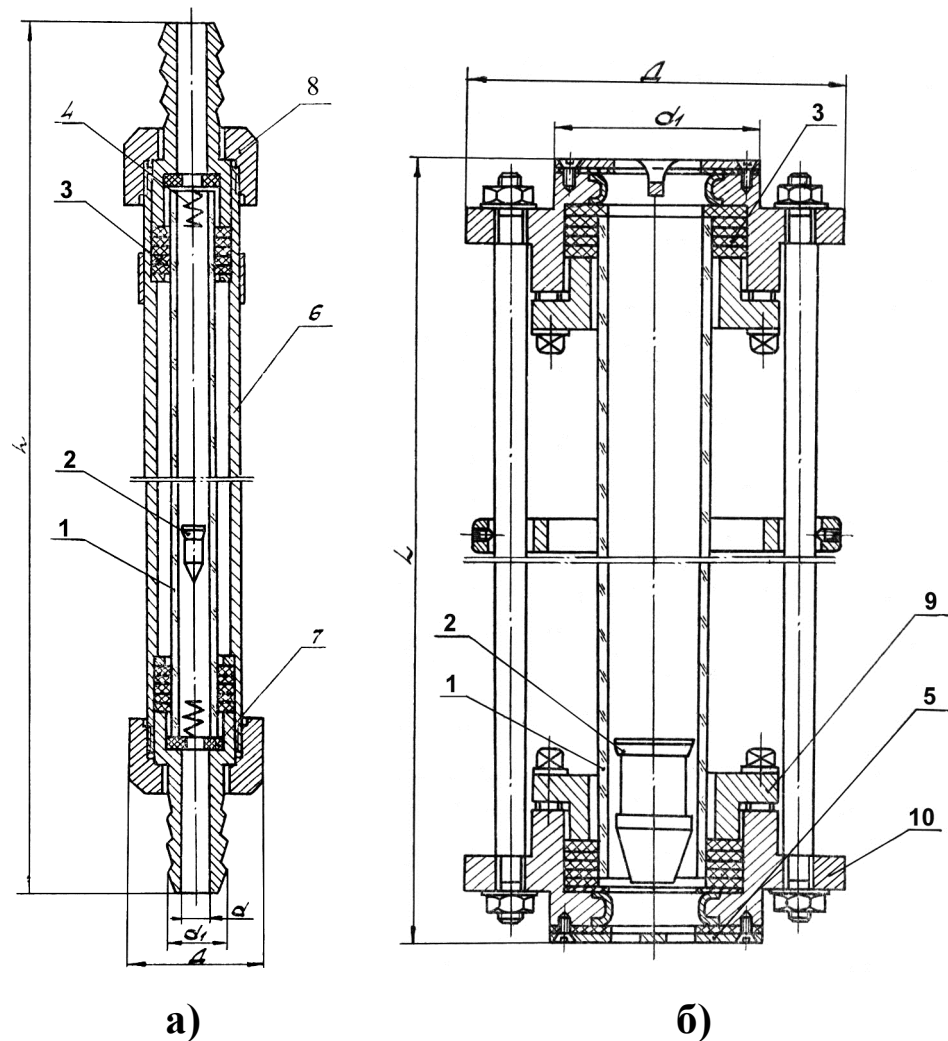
Ротаметр для місцевого вимірювання витрати типу РМ: 1 – трубка рота метрична; 2 – поплавок; 3,7 – прокладка; 4 – упор; 5 – діафрагма; 6 – обойма; 8 – гайка; 9 – фланець; 10 – корпус.
